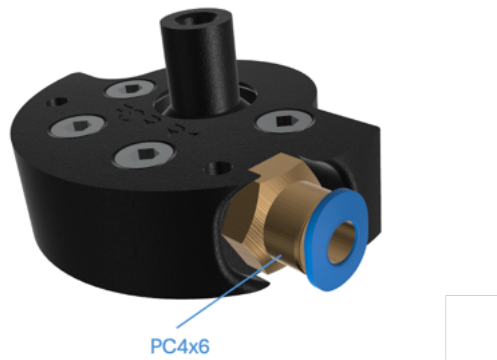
Rewinder-Chassis Montageschritt 17.
